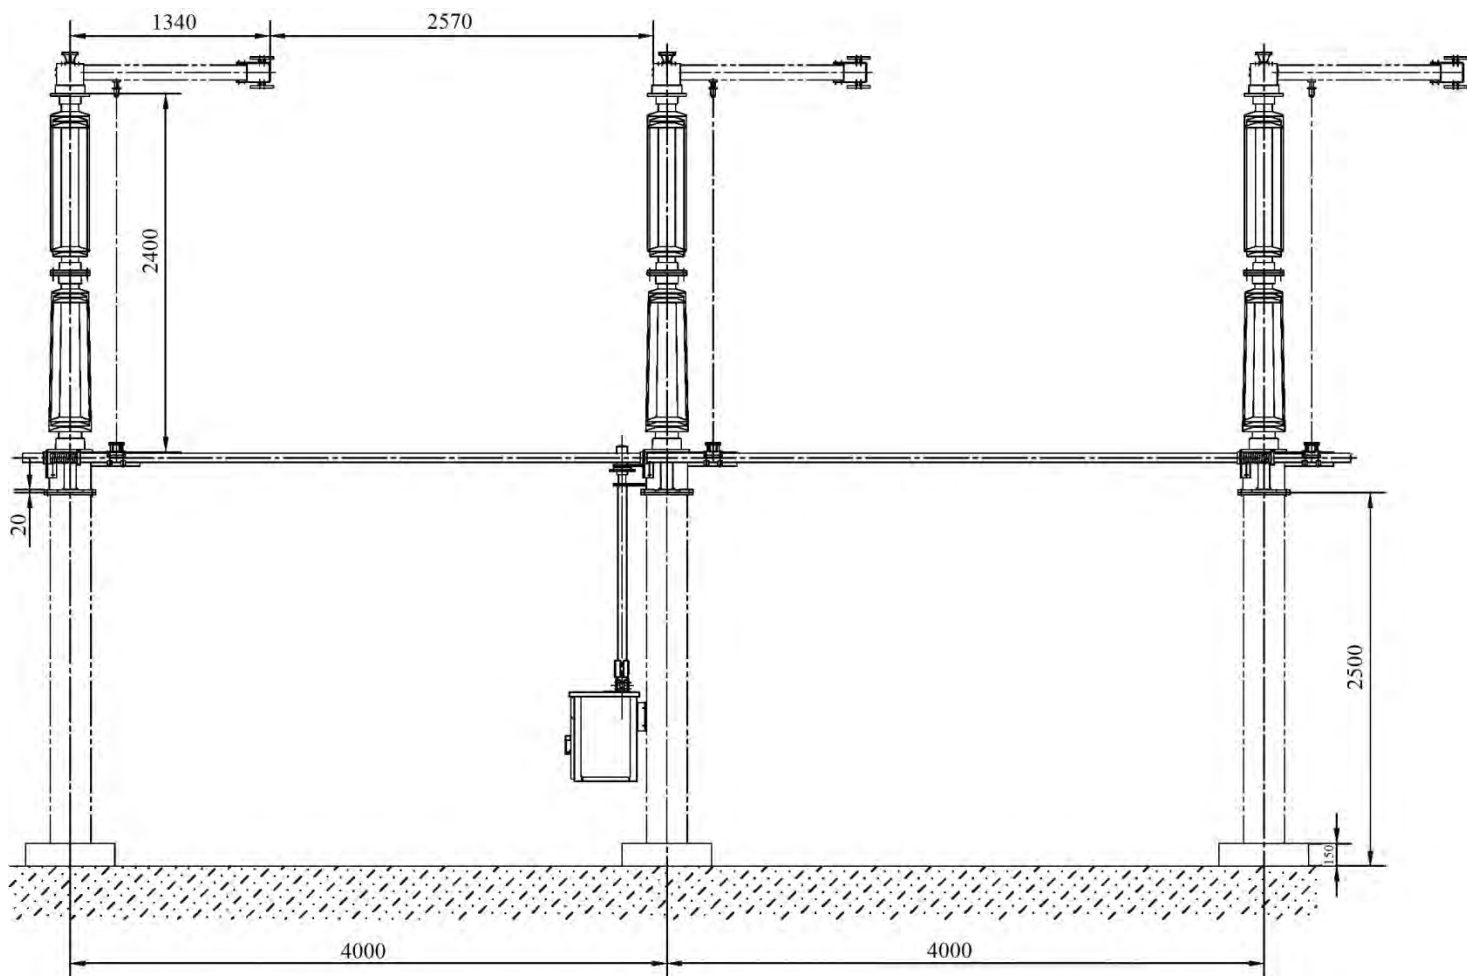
Габаритные размеры и конструктивное исполнение разъединителя РГП на напряжение 220 кВ
